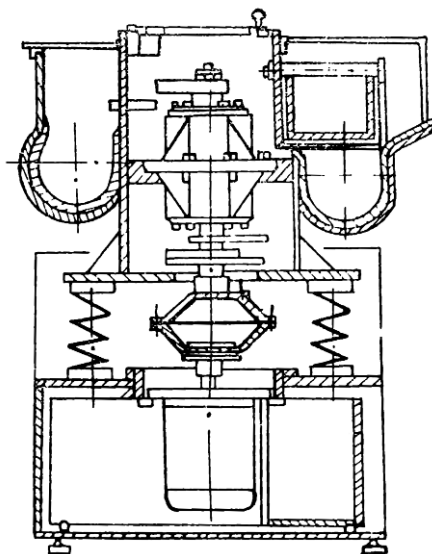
Схема галтувального станка с тороподібною робочою камерою
